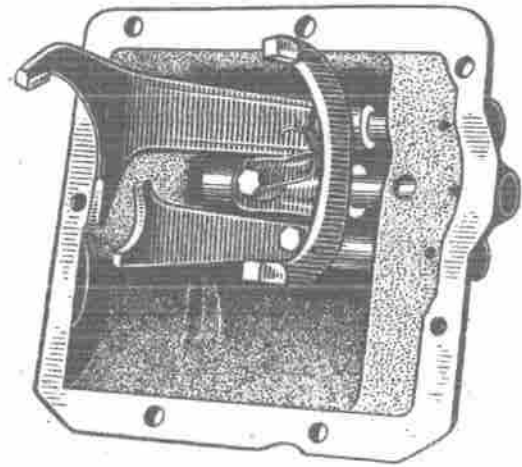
Drahtsicherung für Befestigungsschrauben der Schaltgabel
